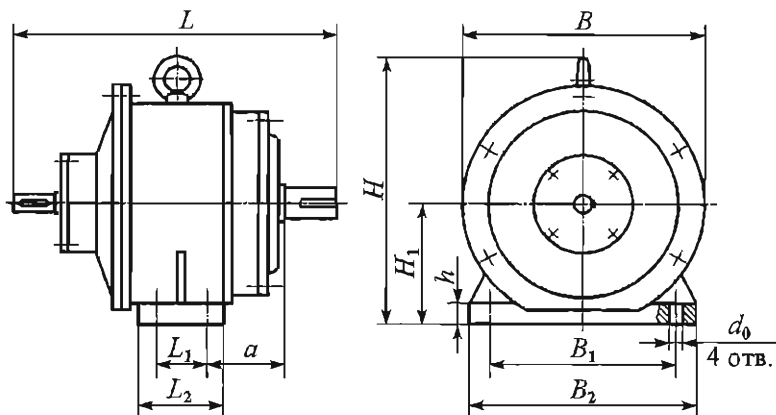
Габаритные, установочные и присоединительные размеры редуктора
